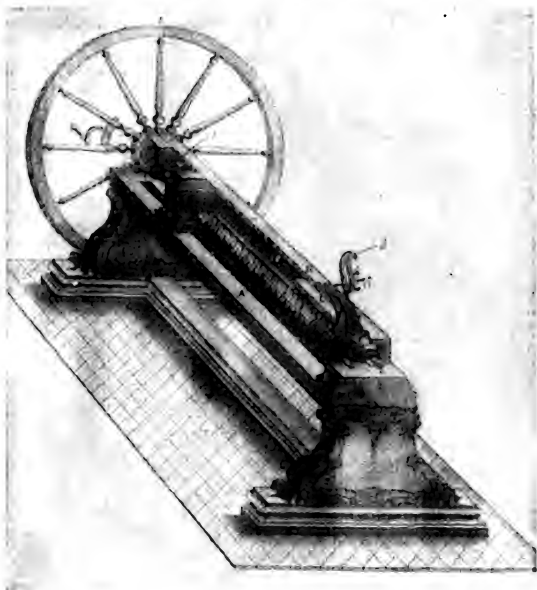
Токарно-винторезный станок с механизмованным суппортом и сменными шестернями, предназначенный для производства деталей машин. Конструкция А. К. Нартова. 1738 г. Рукопись «Театрум Махинарум» А. К. Нартова.
